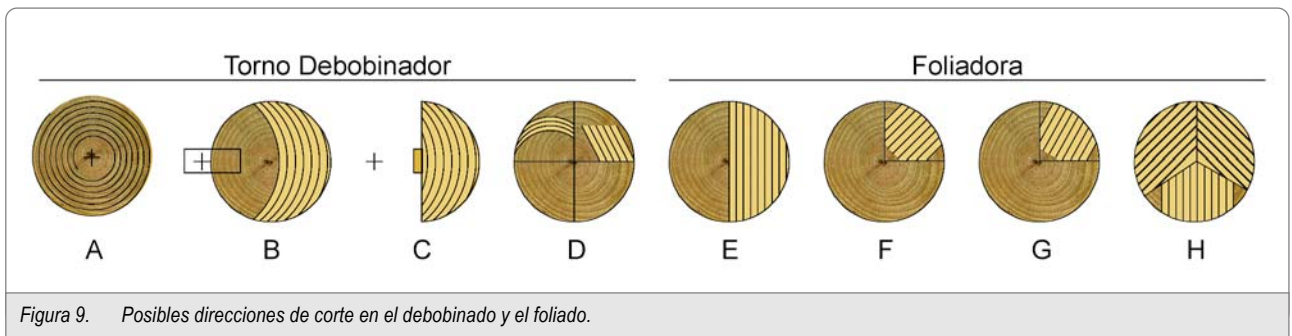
Posibles direcciones de corte en el debobinado y el foliado.
